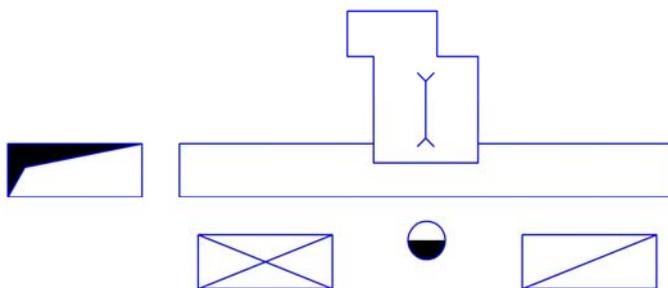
Организация рабочего места станка ЦМЭ-3 рычажно-шарнирного (маятникового) для чернового раскроя заготовок на детали
